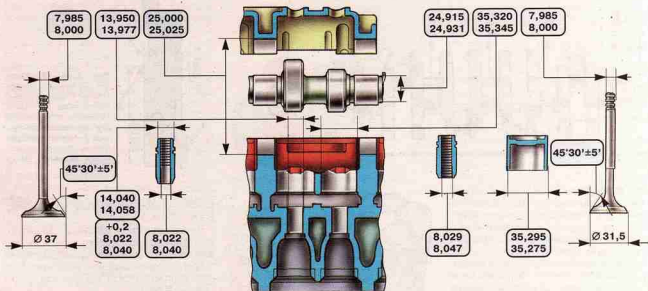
Основные размеры головки цилиндров и деталей механизма привода клапанов, мм
